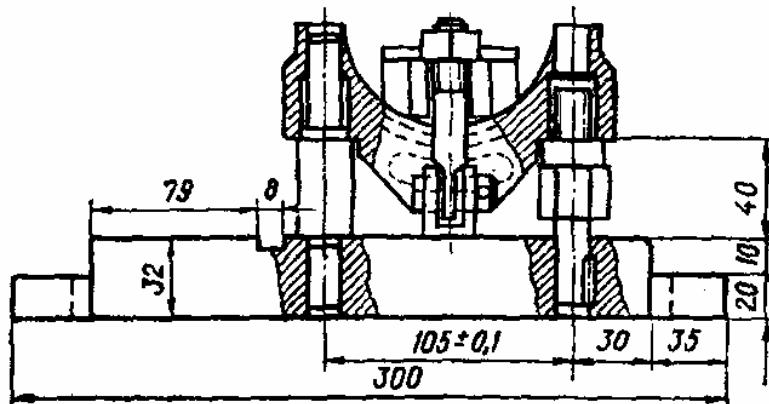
Пристрій для встановлення кришки шатуна під час фрезерування (шліфування) поверхонь рознімання
